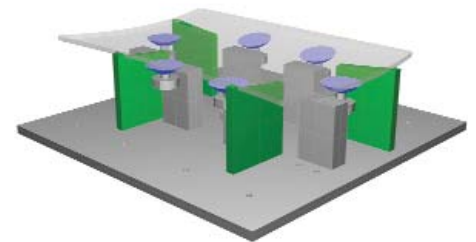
Spannvorrichtung für eine Magnesium-Modellmotorhaube zum 3D-Laserstrahlschweißen
